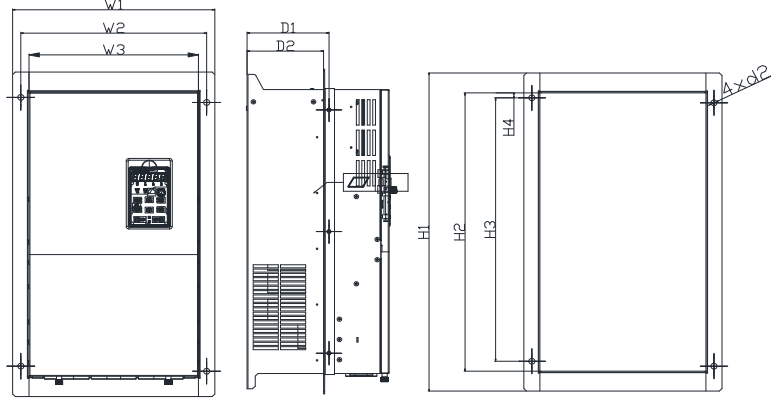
4 ~ 30 kW Flanş montajı kurulum şeması
